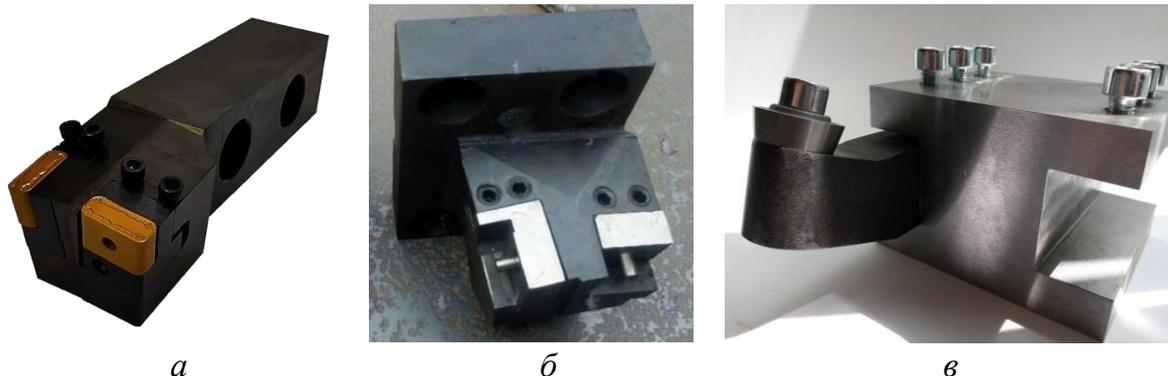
Различные конструкции резцов с СМП для обработки бандажей колесных пар: *a* – резец с тангенциальным креплением СМП; *б* – резцовая головка с тангенциальным креплением СМП; *в* – резец с радиальным креплением СМП
